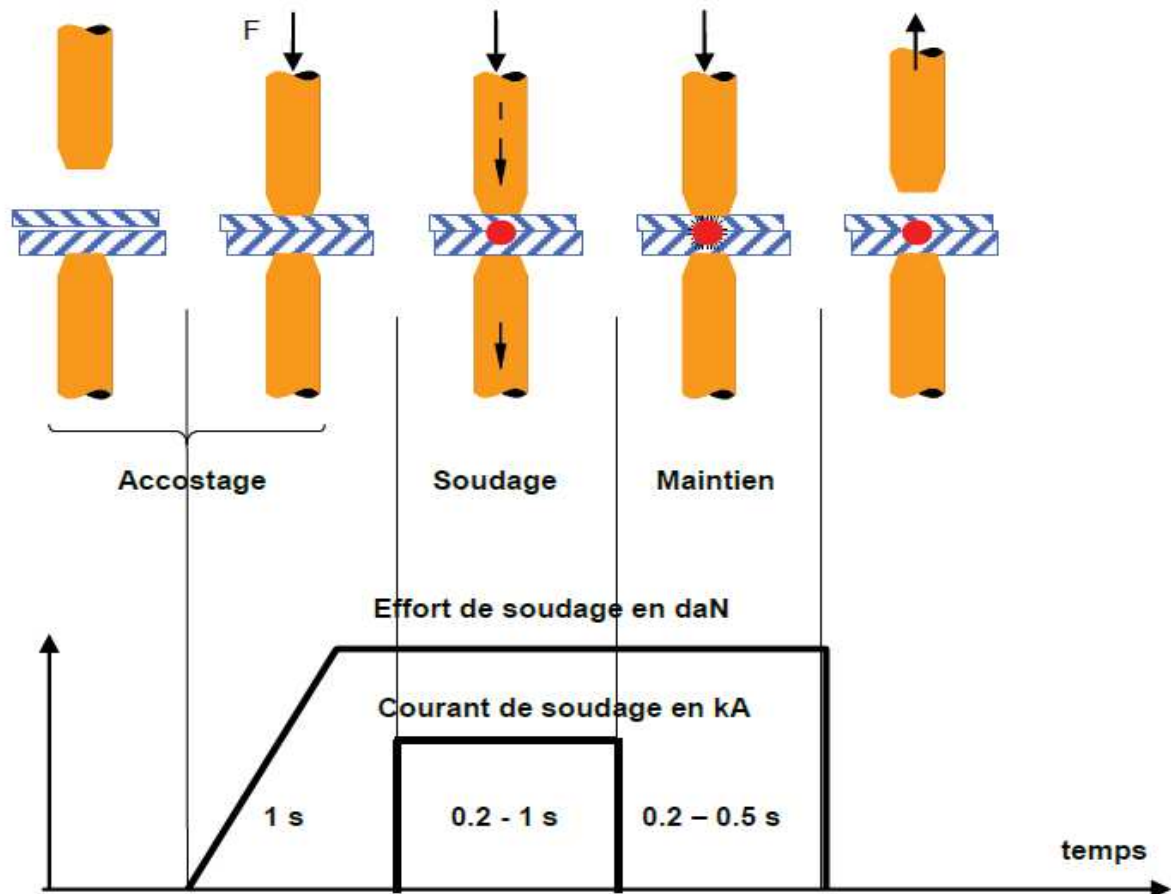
Principe et phases successives du procédé de soudage par points [1].
